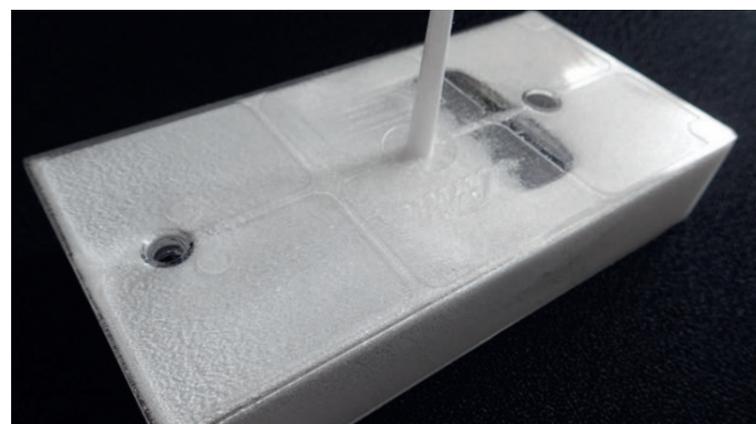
Mit circa 16 Prozent Gewichtseinsparung auf Standard-spritzgießmaschine physikalisch geschäumtes PC-Bauteil mit glatter Oberfläche durch Gasgegendruck
